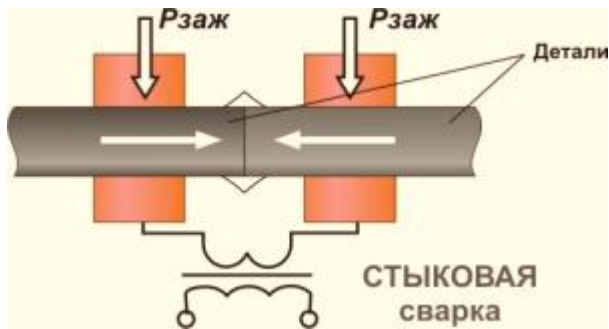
Контактная сварка стыковая, точечная, шовная
